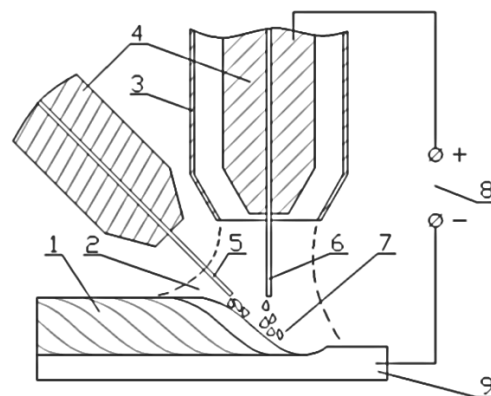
Схема процесса сварки в защитных газах с ДПП: 1 – наплавленный металл; 2 – защитная атмосфера; 3 – сопло; 4 – наконечник; 5 – дополнительная электродная проволока; 6 – основная электродная проволока; 7 – сварочная ванна; 8 – источник питания; 9 – свариваемый металл
